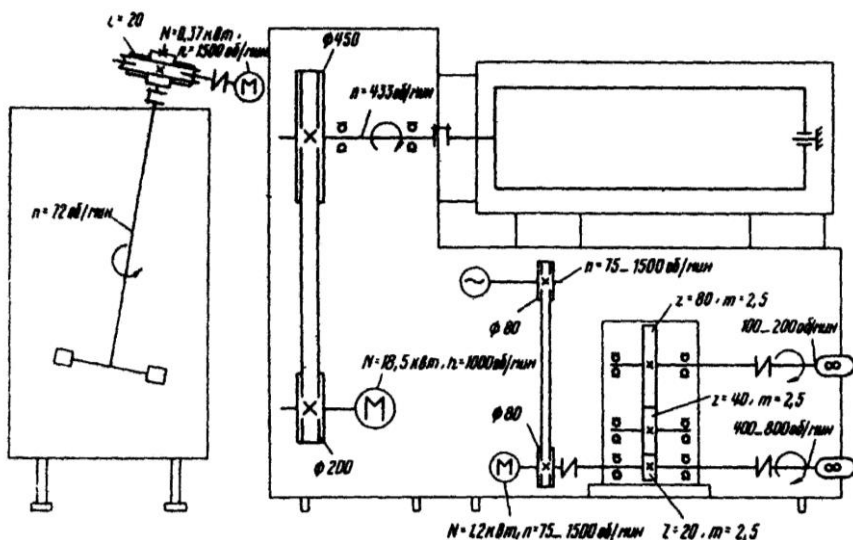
Кінематична схема фризера марки Б6-ОФШ
